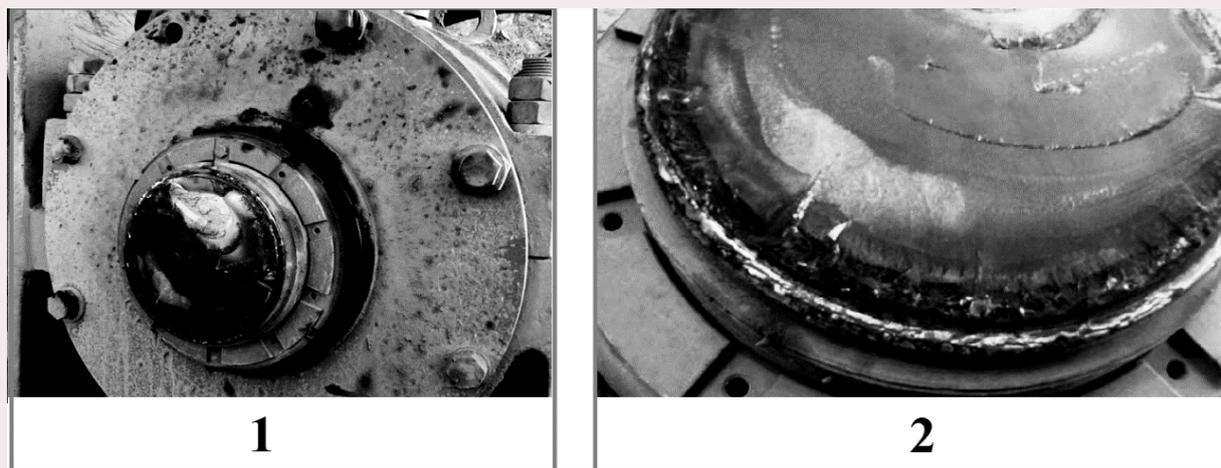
Общий вид щековой дробилки СМД111 после аварии
